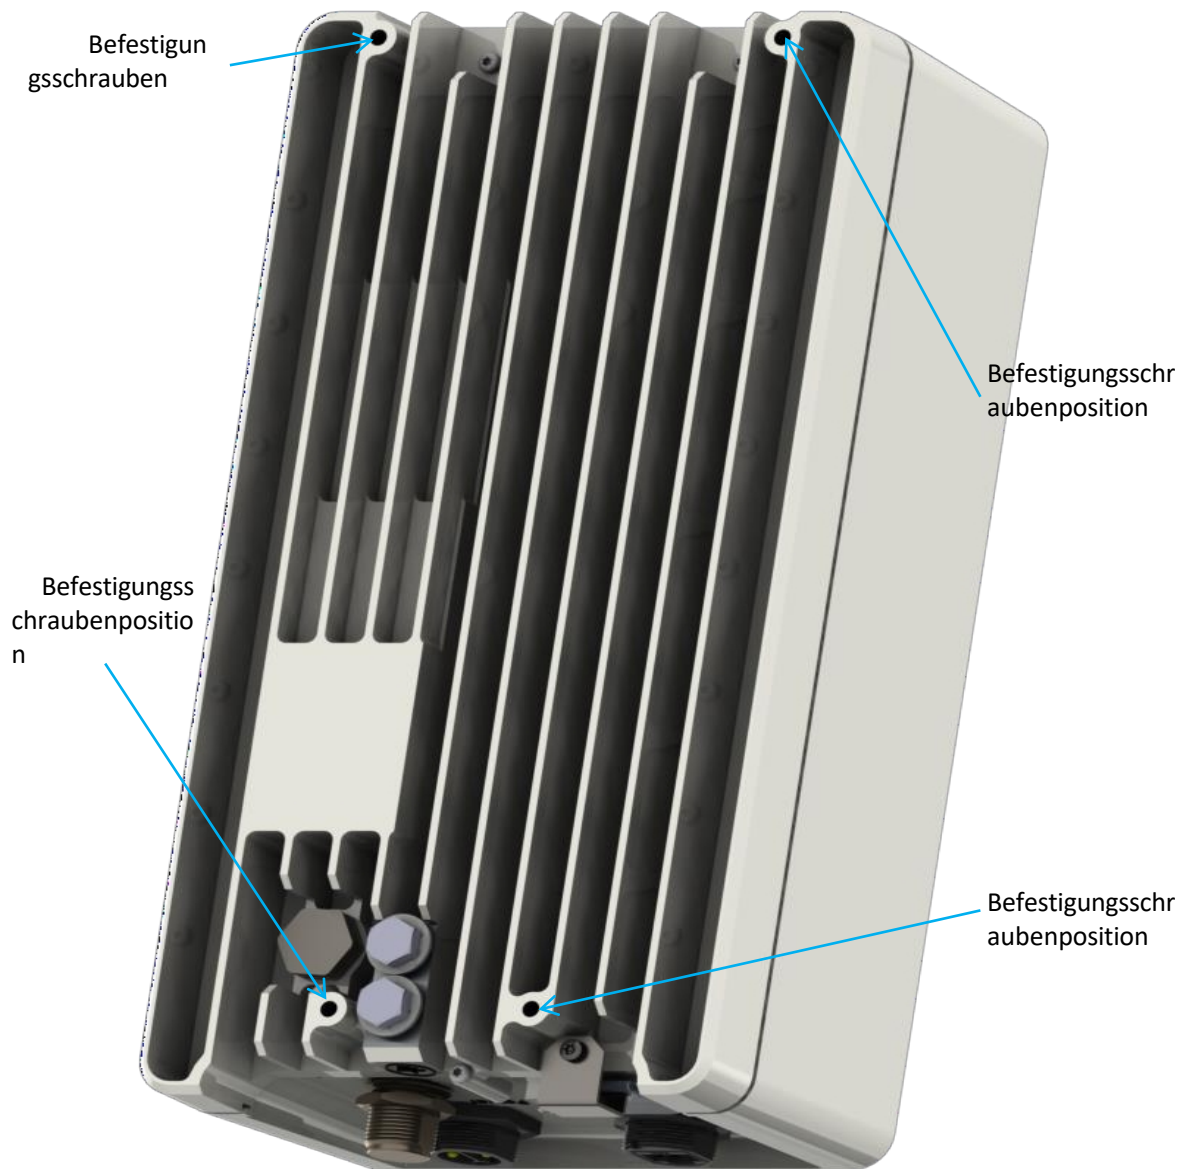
Befestigungsschraubenpositionen der Halterung für das Kona Macro Gateway
